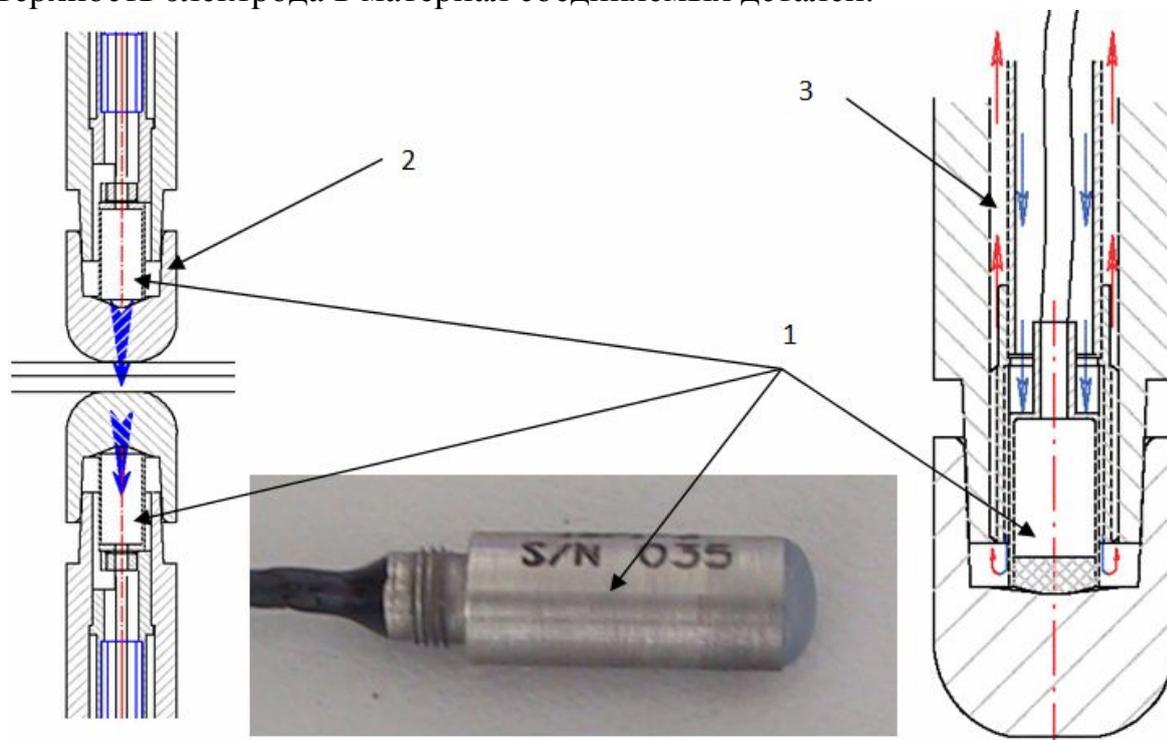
Активный ультразвуковой метод контроля процесса КТС: 1) ультразвуковой преобразователь; 2) сменный наконечник сварочного электрода; 3) канал охлаждения
